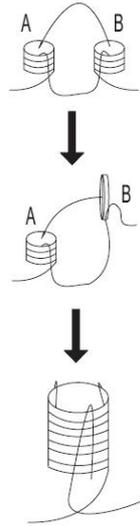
Instrucciones para cables de soldadura
